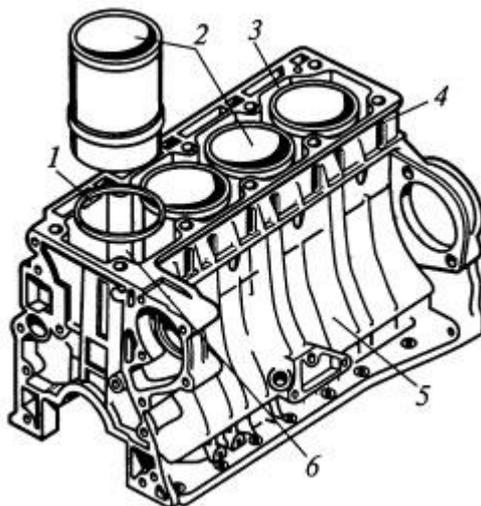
2. Блок двигателя со съемными гильзами цилиндров:
